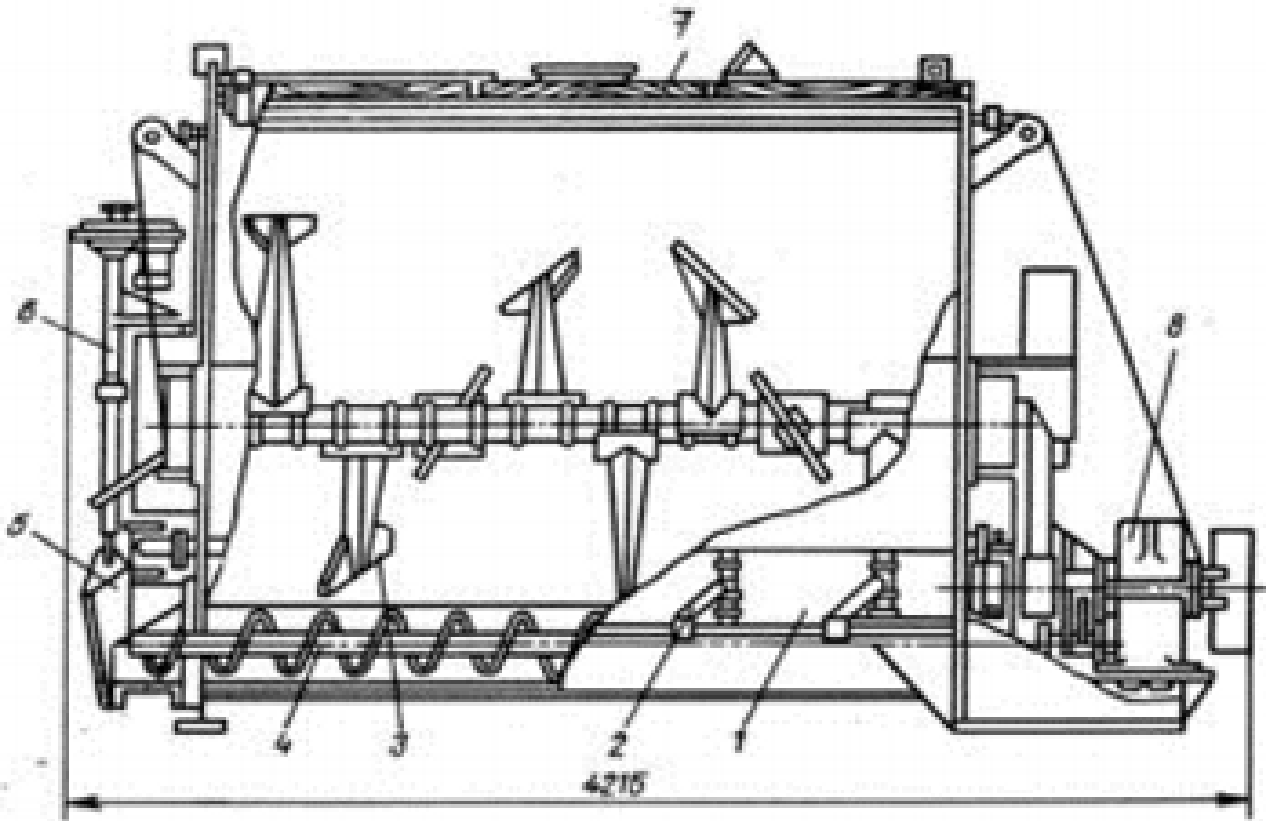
Схема змішувача С-12: 1 – корпус; 2 – паророзподільник;
